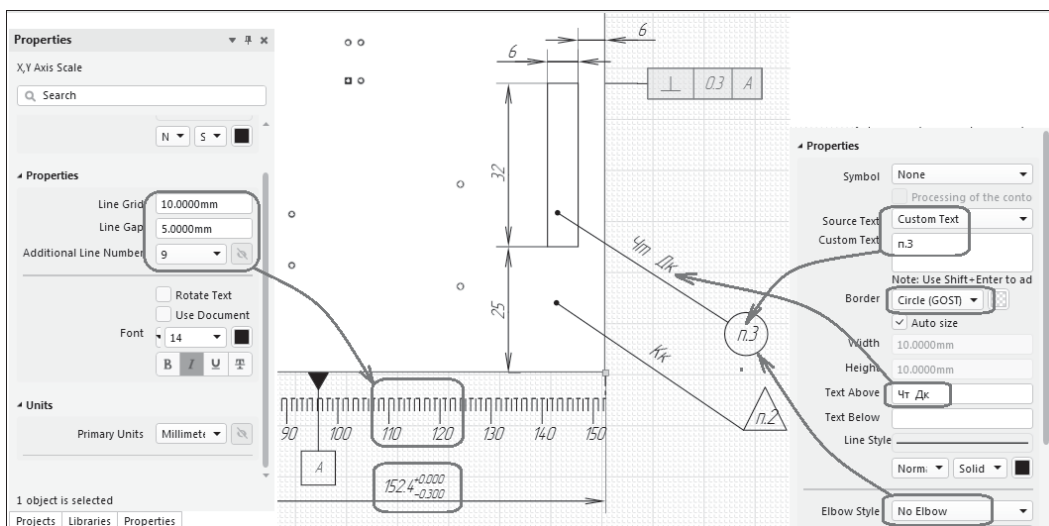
Настройка обозначений координат, знаков маркировки и клеймения: координатные линейки (слева); обозначения маркировки и клеймения (справа)
